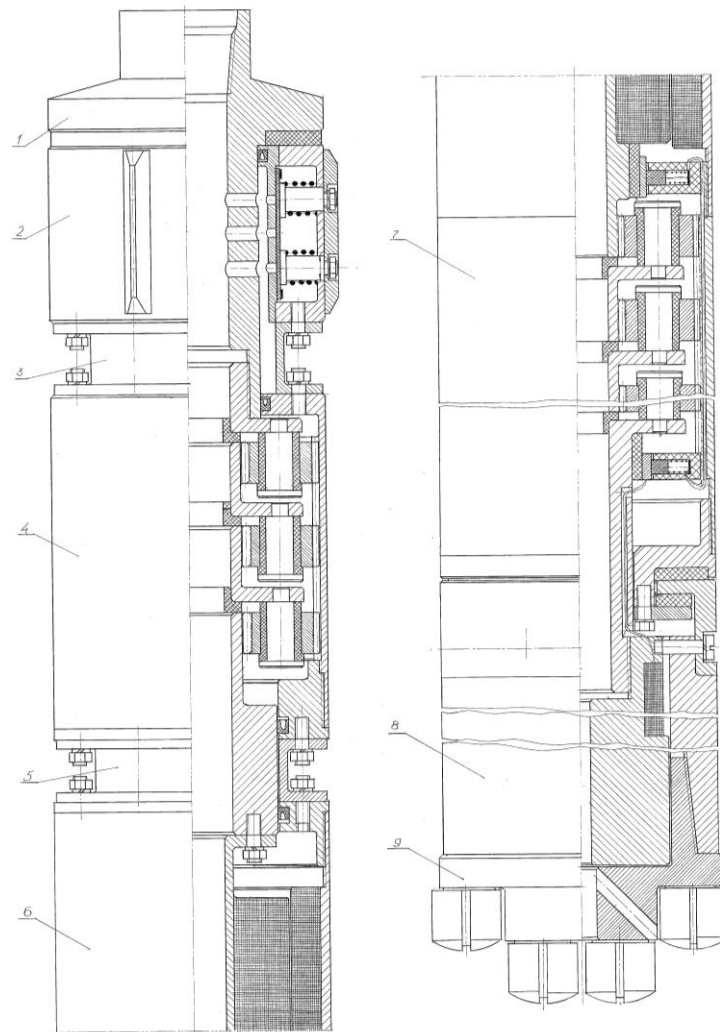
Снаряд термомеханічного буріння : 1 – вал; 2 – пневматичний розкріплюючий пристрій; 3 – фланець; 4 – підвищувальний мультиплікатор; 5 – корпус снаряда; 6 – ротор генератора; 7 – понижуючий мультиплікатор; 8 – магнетрон; 9 – планетарне двоступінчасте долото.
